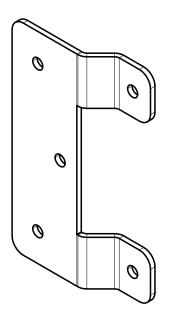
Montage mural X-300EEC (cotes en mm)
